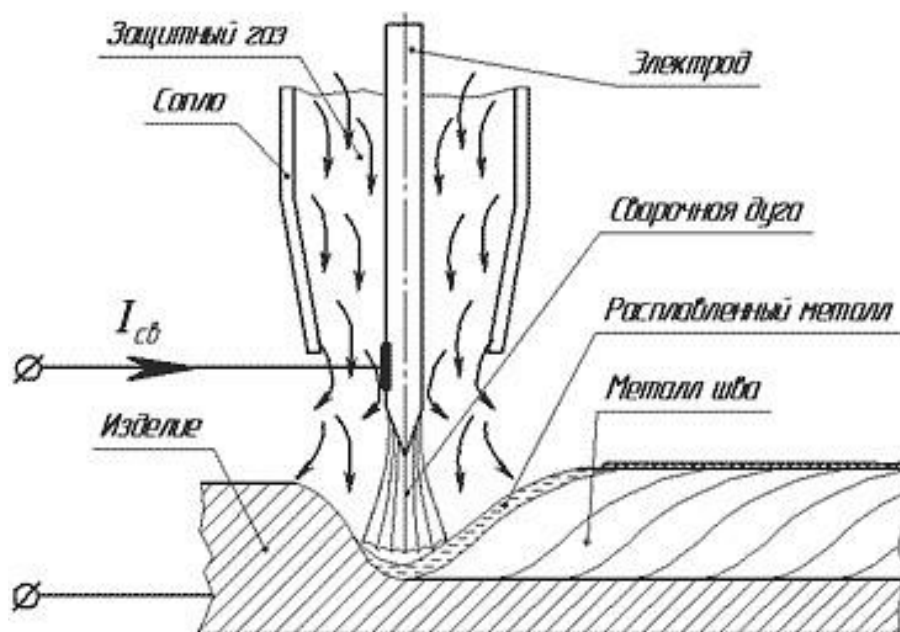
Схема сварки неплавящимся электродом
